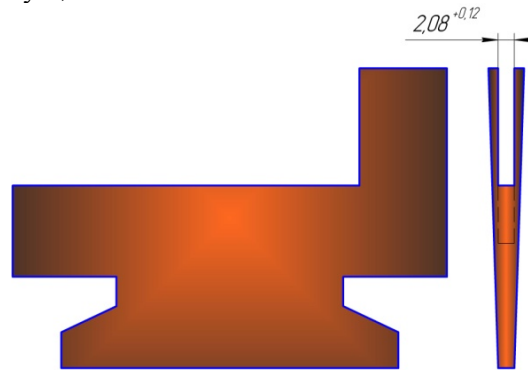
Заготівка колекторної пластини з прорізанним шліцом
